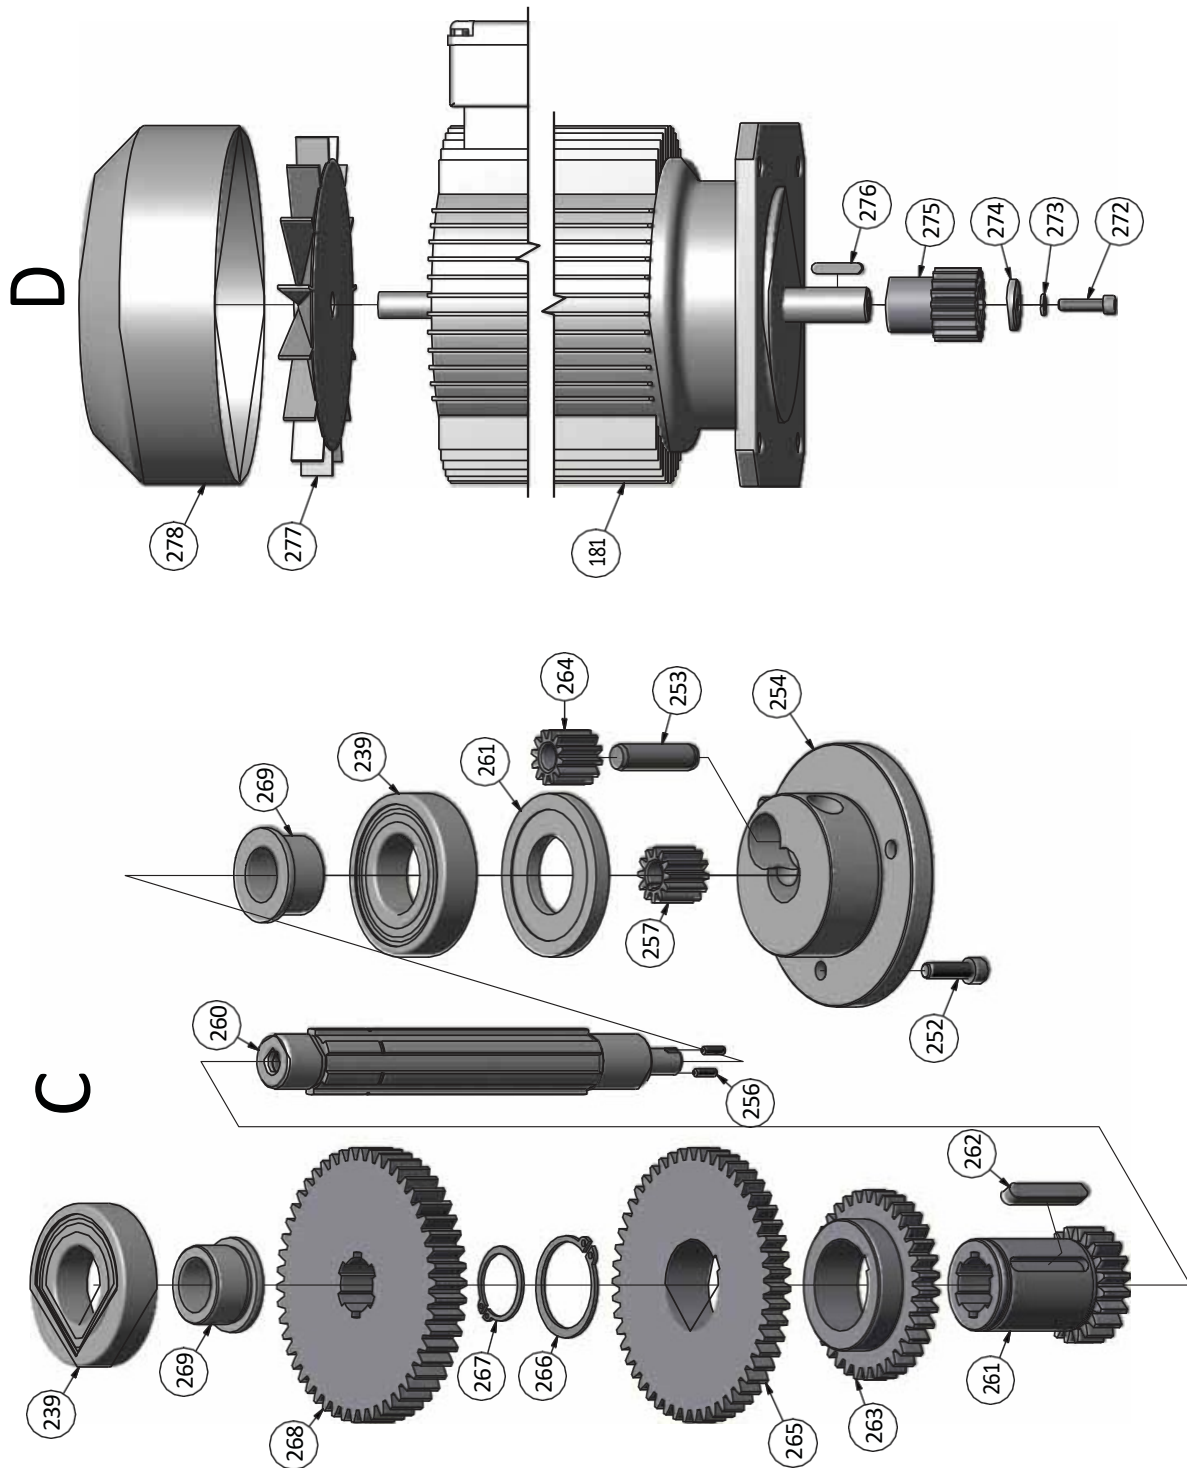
Getriebe Bohrspindel 2 von 4 - Gearbox main spindle 2 von 4
